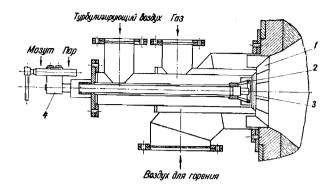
Газомазутные горелки типа ГМГ и НГМГ: I— регистры воздуха, подаваемого на горение; 2— регистры турбулизирующего воздуха; 3— коническое кольцо с отверстиями для выхода газа; 4— мазутиля форсунка.
